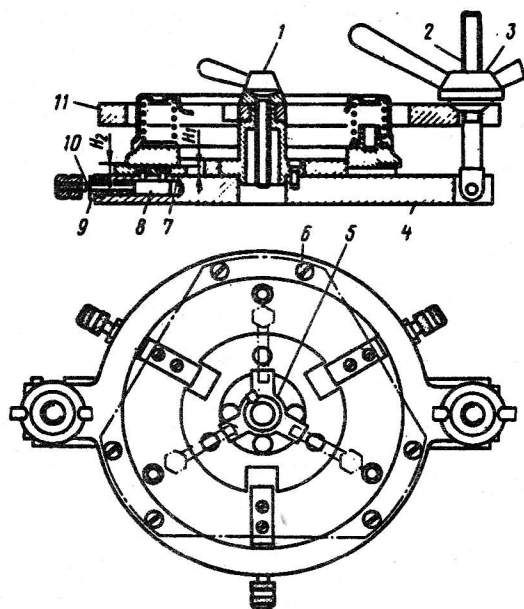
Приспособление 7820-5079 для разборки и сборки нажимного диска сцепления:
